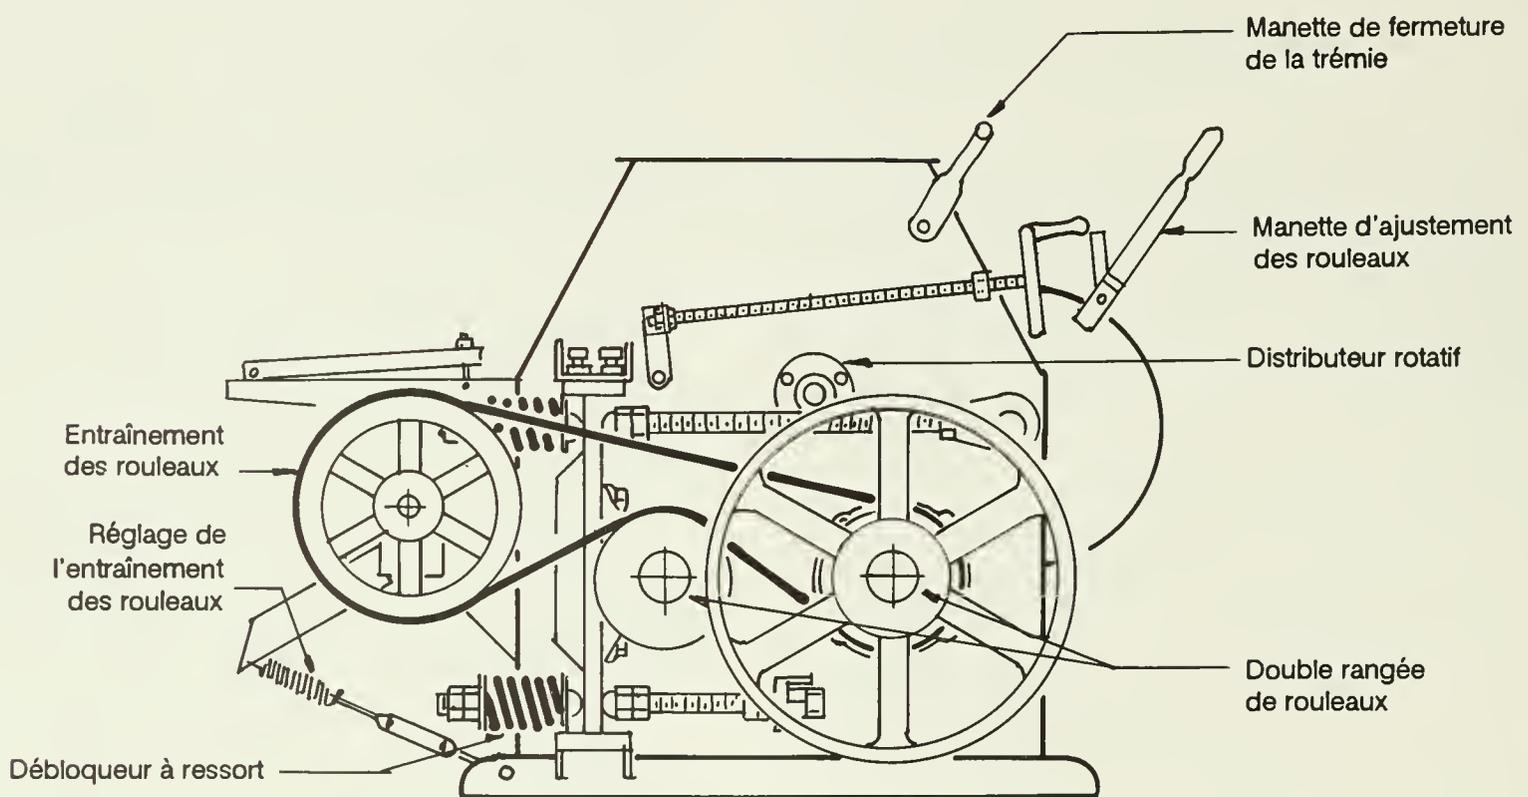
Vue latérale d'une rouleuse industrielle. Source : Roskamp Manufacturing, Inc.
